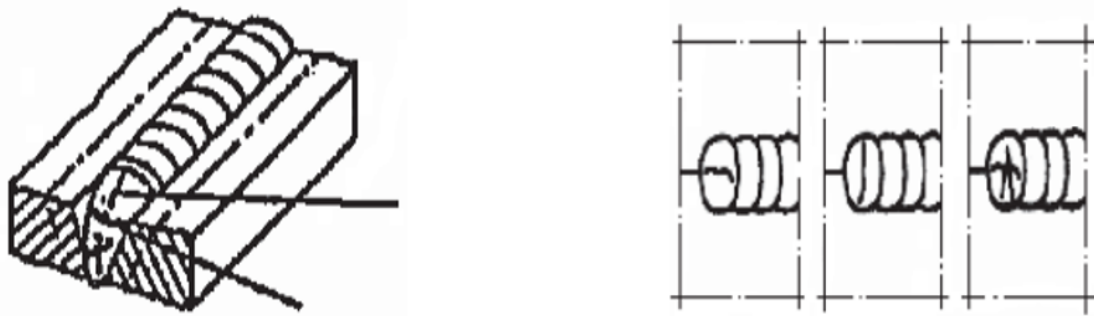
Эскиз дефекта сварного шва
